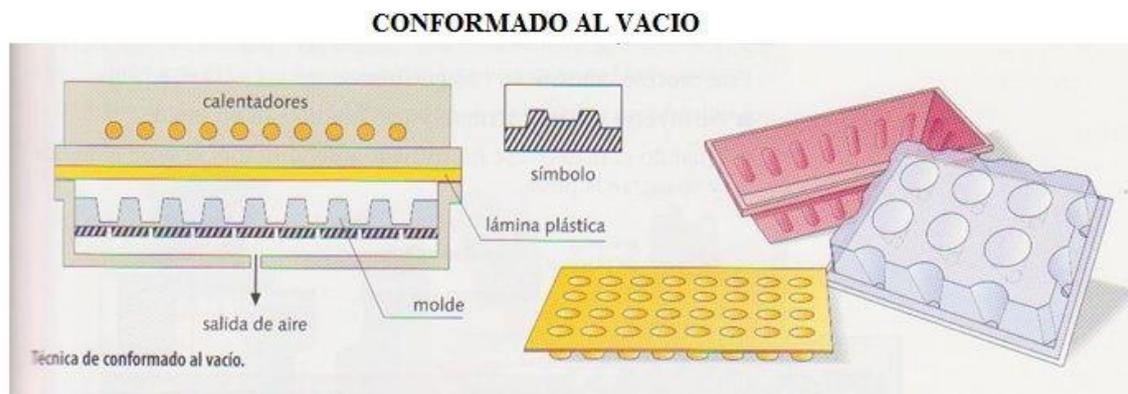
técnica de conformado con ejemplos de productos y símbolo técnico. Fuente: wordpress [4]
